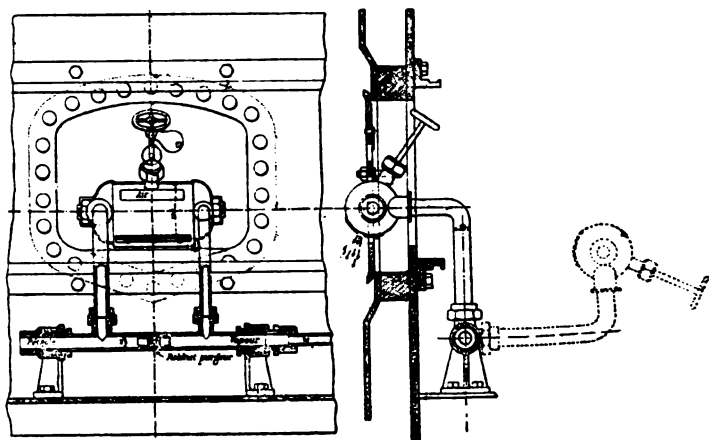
Disposition d'ensemble du foyer Karapetof.
